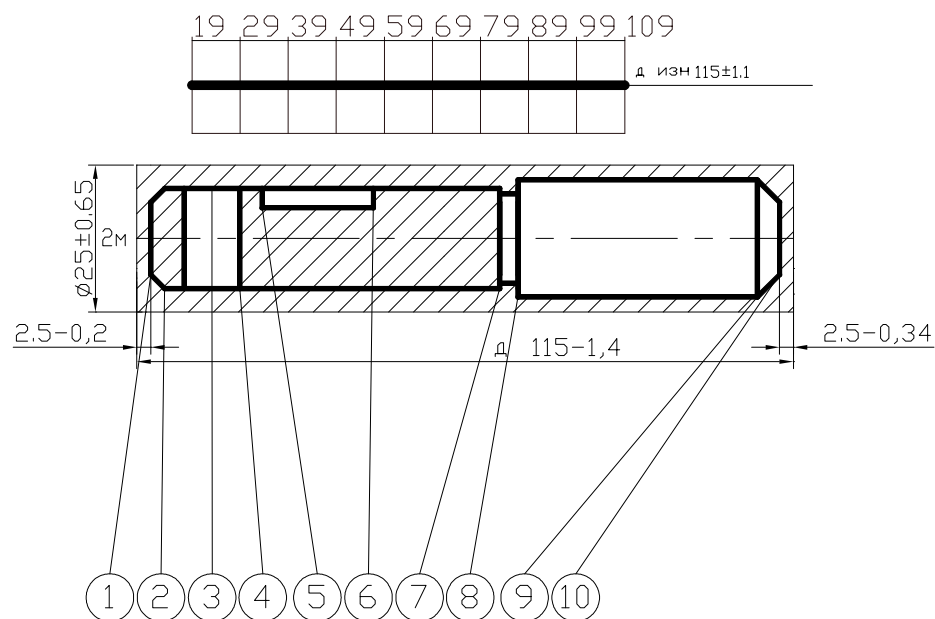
Преобразованный чертёж заготовки (первая проекция)
